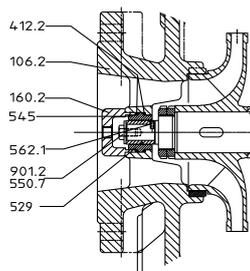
Smontaggio cuscinetto a scorrimento - bocca aspirante assiale
